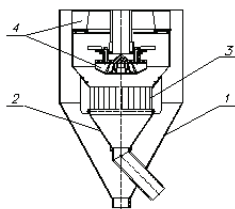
Циркуляционный сепаратор: 1 — наружный конус; 2 — конус грубого продукта; 3 — направляющие; 4 — вентиляторы.
